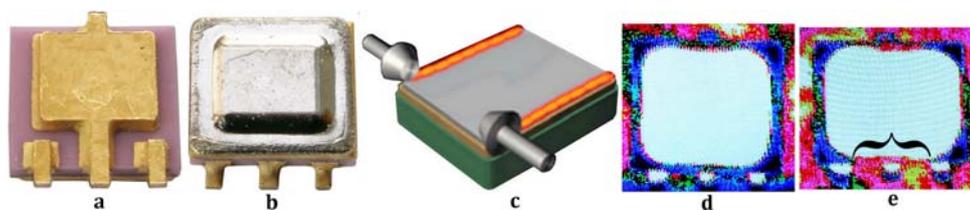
Внешний вид корпуса (а – снизу, b – сверху), схема шовно-роликовой сварки (с), лазерные фотоакустические топограммы герметичного (d) и негерметичного (e) корпусов. Негерметичный участок шва показан фигурной скобкой
